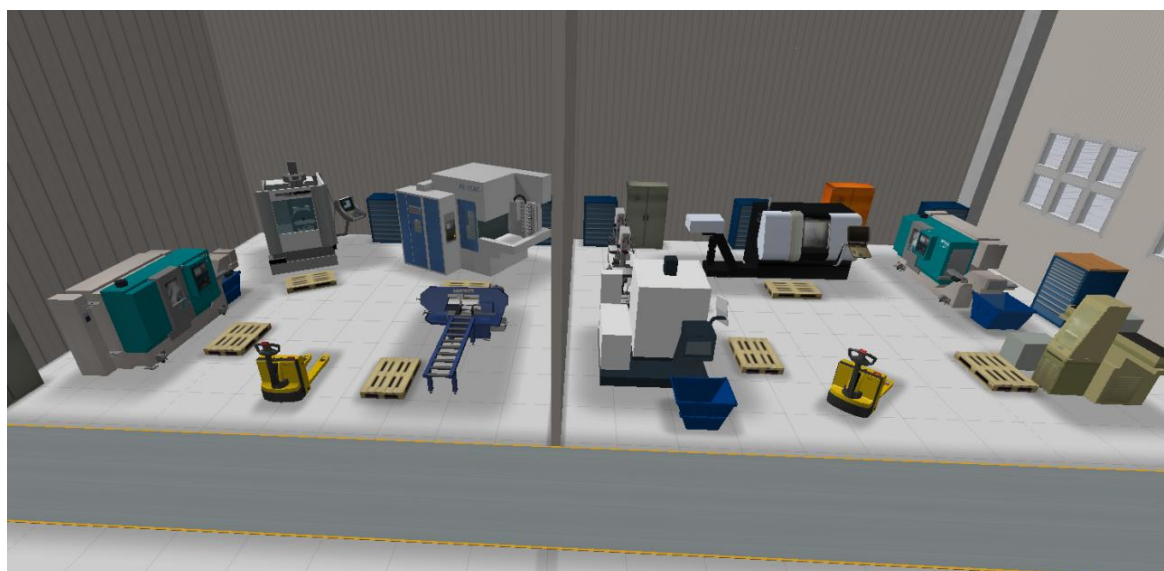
Předmětné uspořádání výroby - 3D layout
